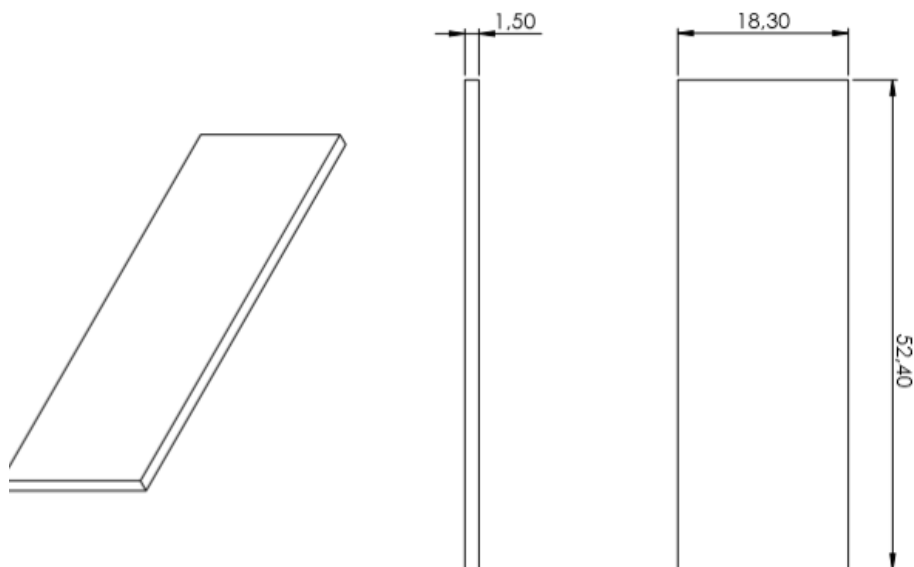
Dimensiones de la placa para la fabricación del elemento 2 de la boquilla
